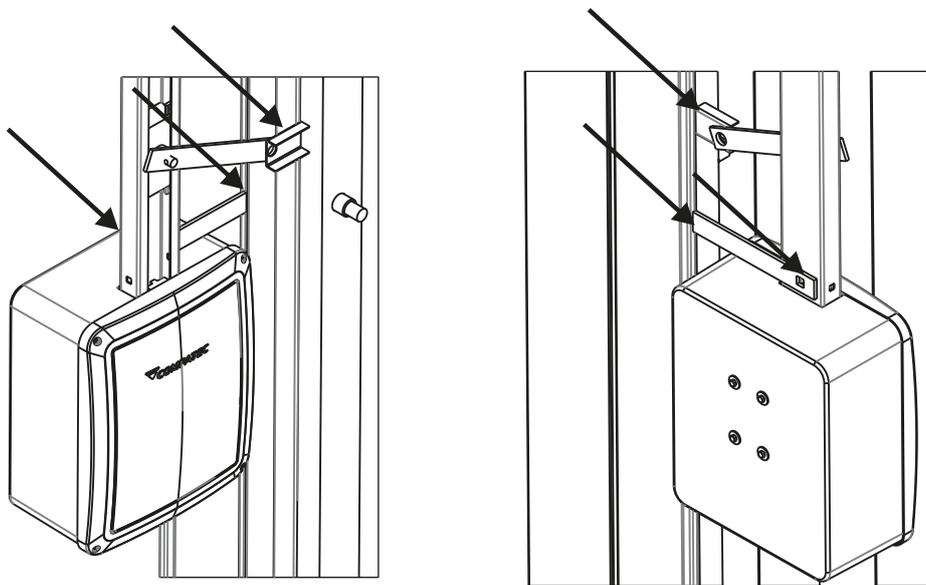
1º Fijar con un pingo de soldadura el "Caballete con Pino" en el "Brazo de Destramado" el "Soporte doblado". 2º Posicionar el "Brazo de Destrotamiento" sobre el pino del "Cierre de la cadena". 3º Con el portón todo cerrado, fijar con pingo de soldadura el "Caballete con Pino" en la parte móvil de la puerta. 4º colocar el "Espejo del Brazo" sobre el "Brazo de Destramado" y colocar el pin de "Cierre del espejo del Brazo".
